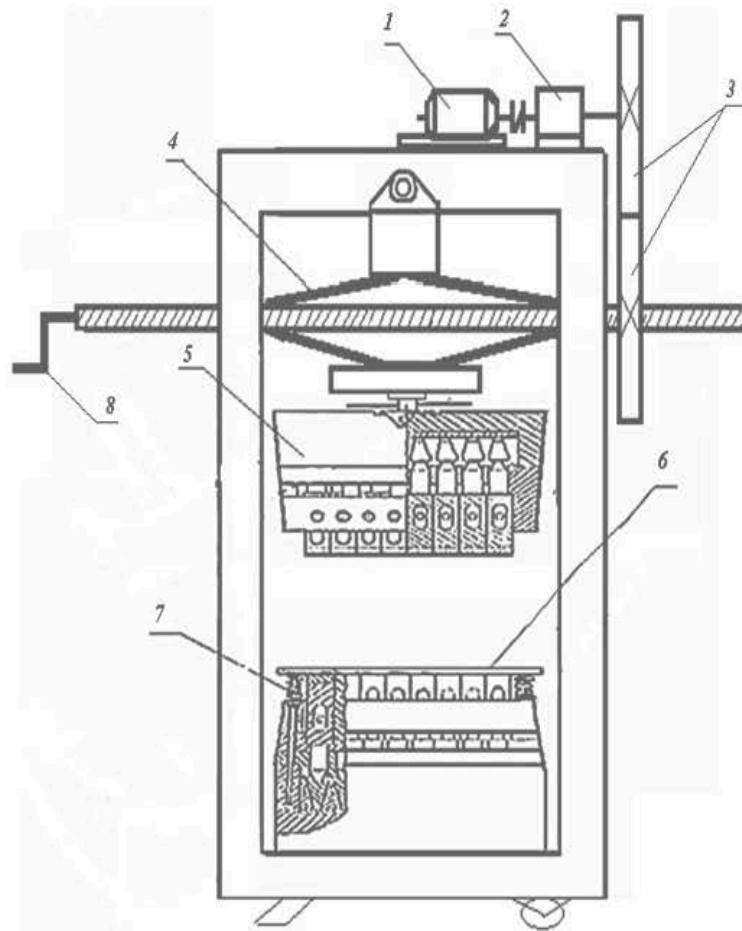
Конструктивная схема механического камнекольного пресса МКП-1
